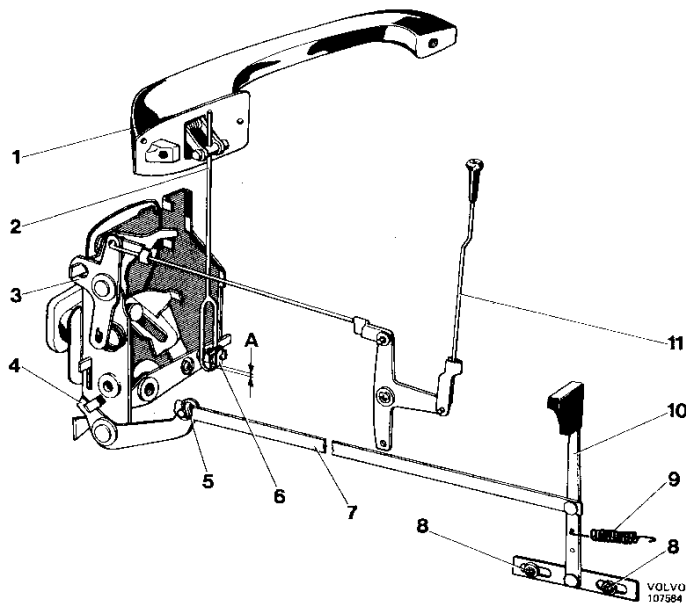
Türschloß, Hintertür (früh. Ausf.)
